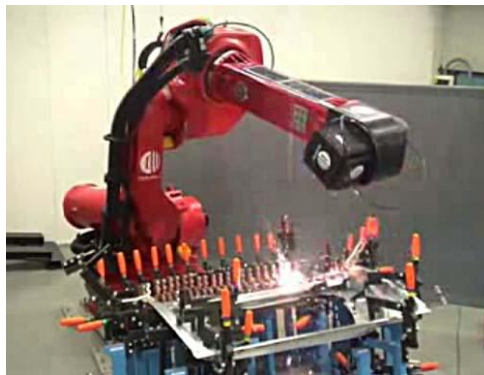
Soldadora por rayo laser análoga automatizada, [\(video\)](#).
